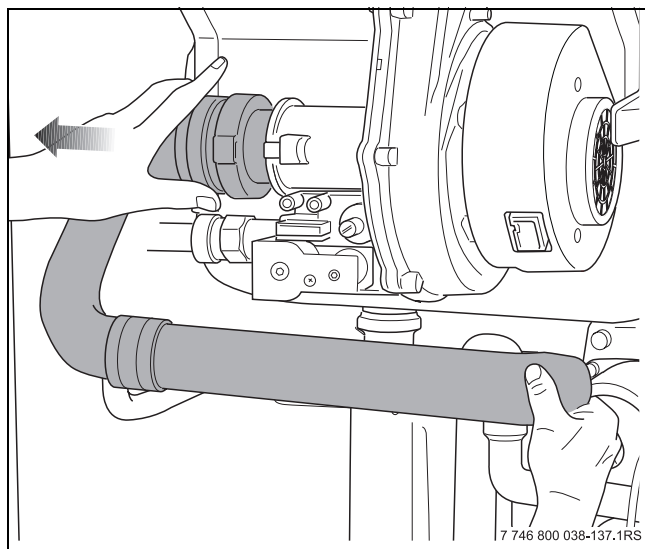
Демонтаж воздухозаборной трубы вентилятора
